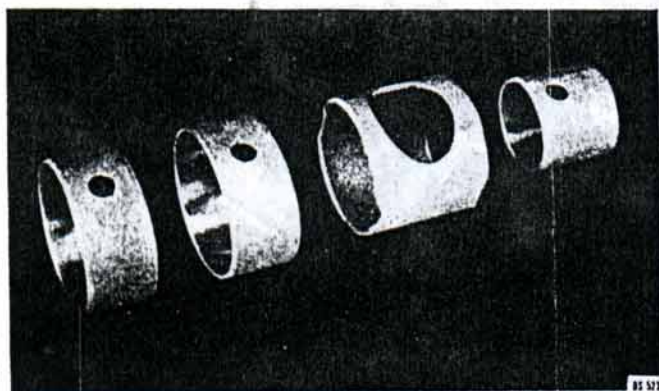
Bujes de árbol de levas para Motor 6L-226.
